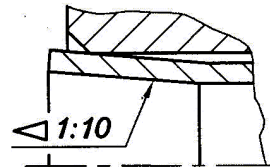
Конічне розвальцьовування труби перед зварюванням
